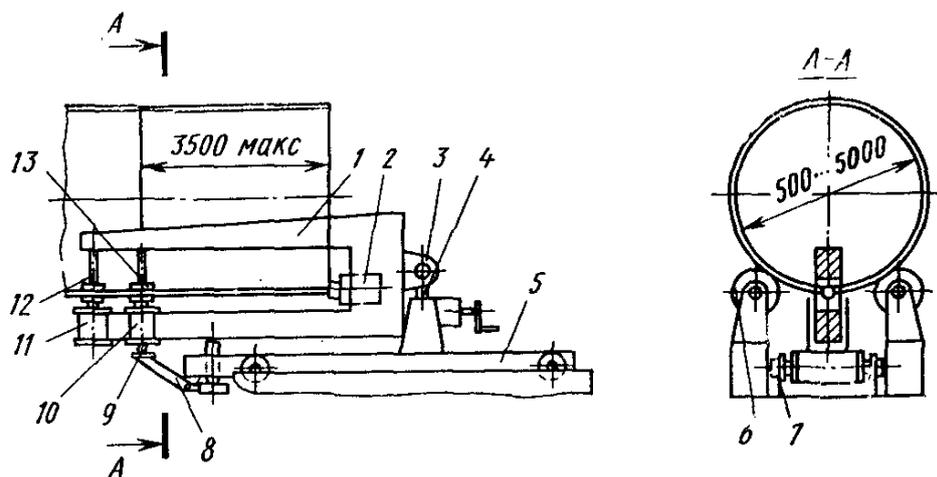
Установка для механизированной сборки кольцевых стыков цилиндрических сосудов
